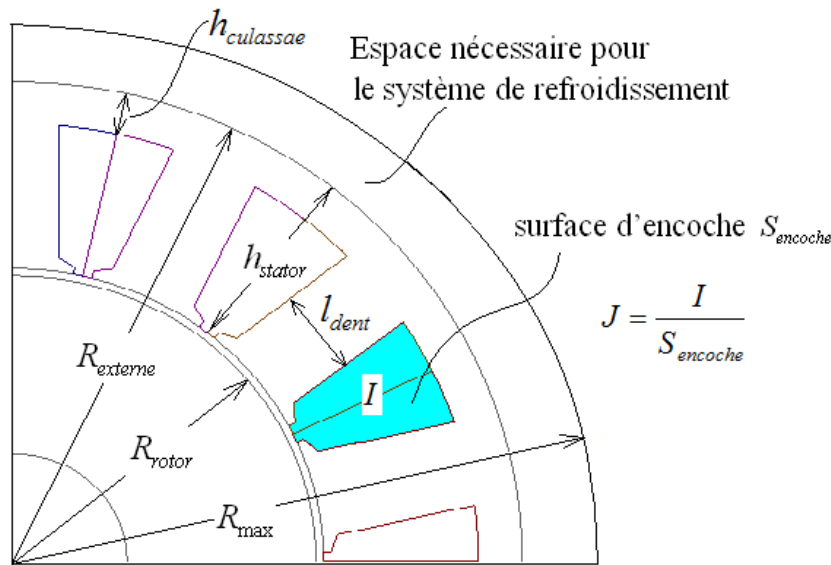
les dimensions principales d'une machine électrique à flux radial
